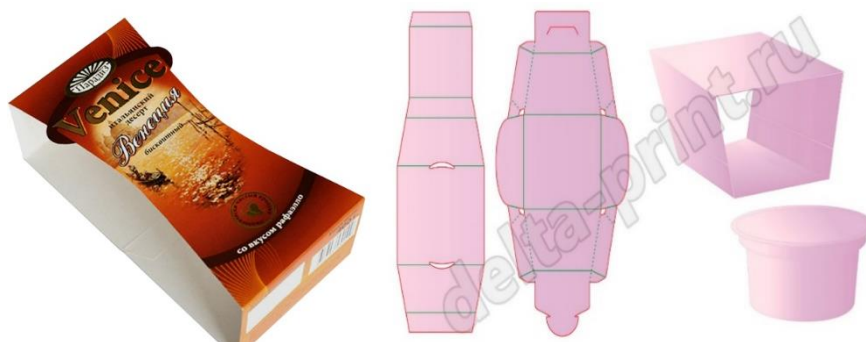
Конструкция и развертка обечайки для картонной коробки
